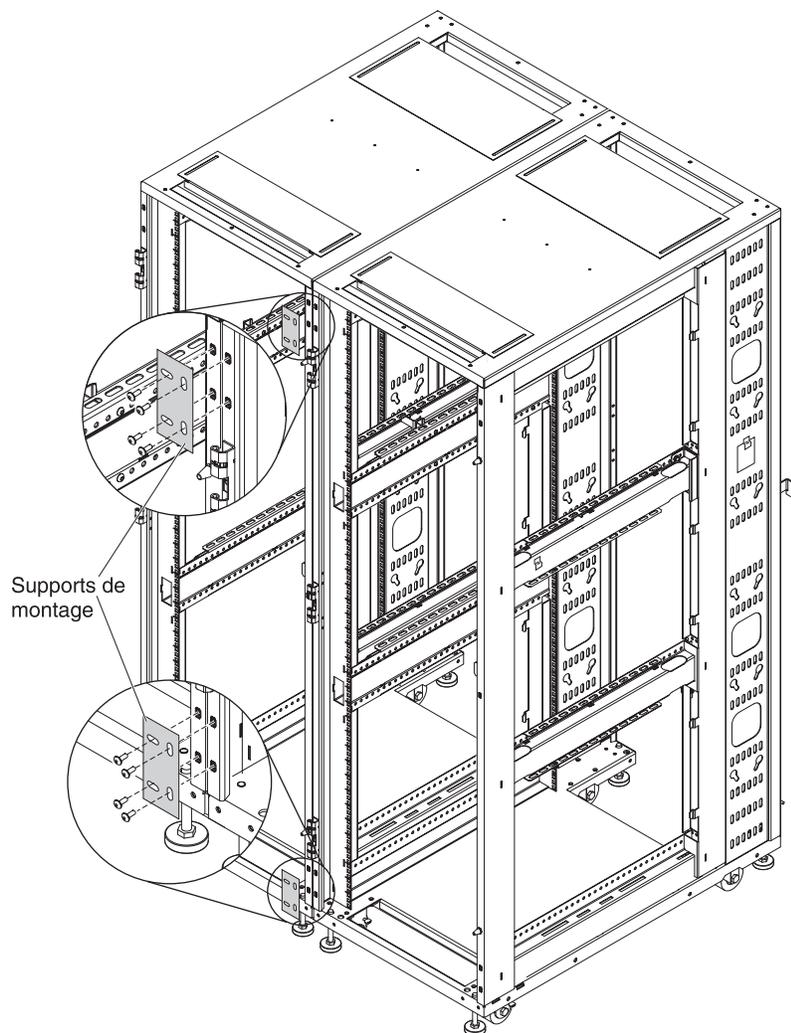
Fixation des armoires standard et à extension entre elles pour constituer une suite
